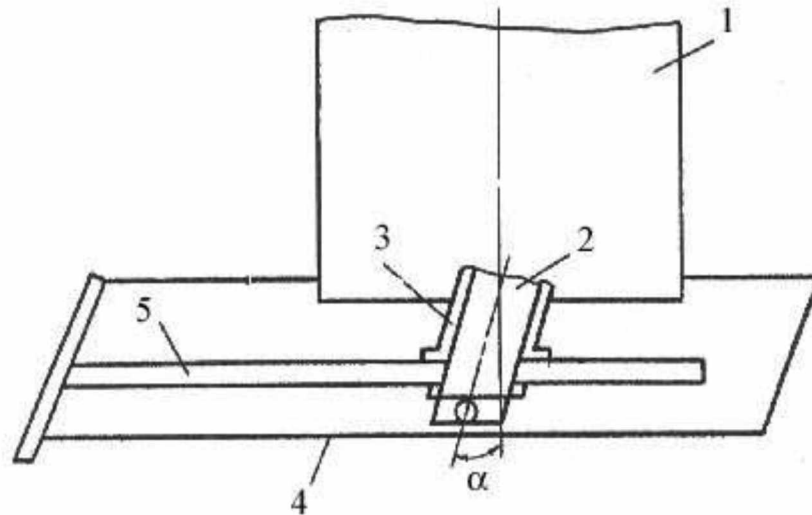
Вібраційний глибокорозпушувач: 1 – верхня частина стійки; 2 – нижня частина стійки; 3 – шарнір; 4 – ріжуча кромка; 5 – лапа
